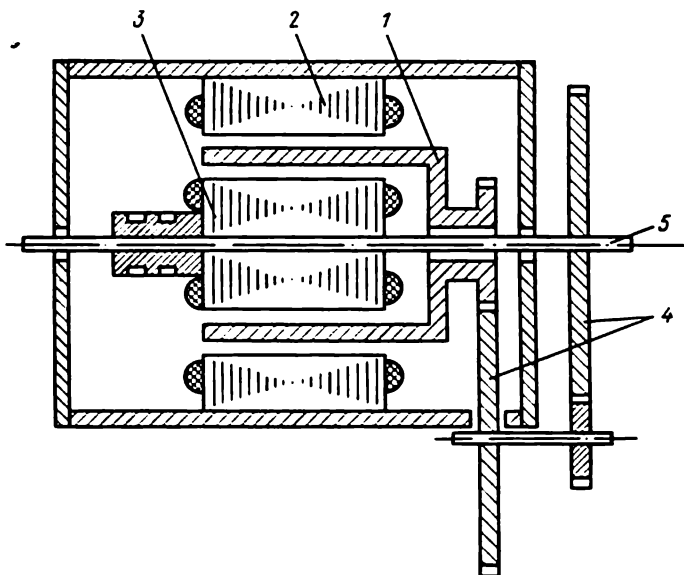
Schéma structural d'une machine combinée: synchro-machine — moteur.
